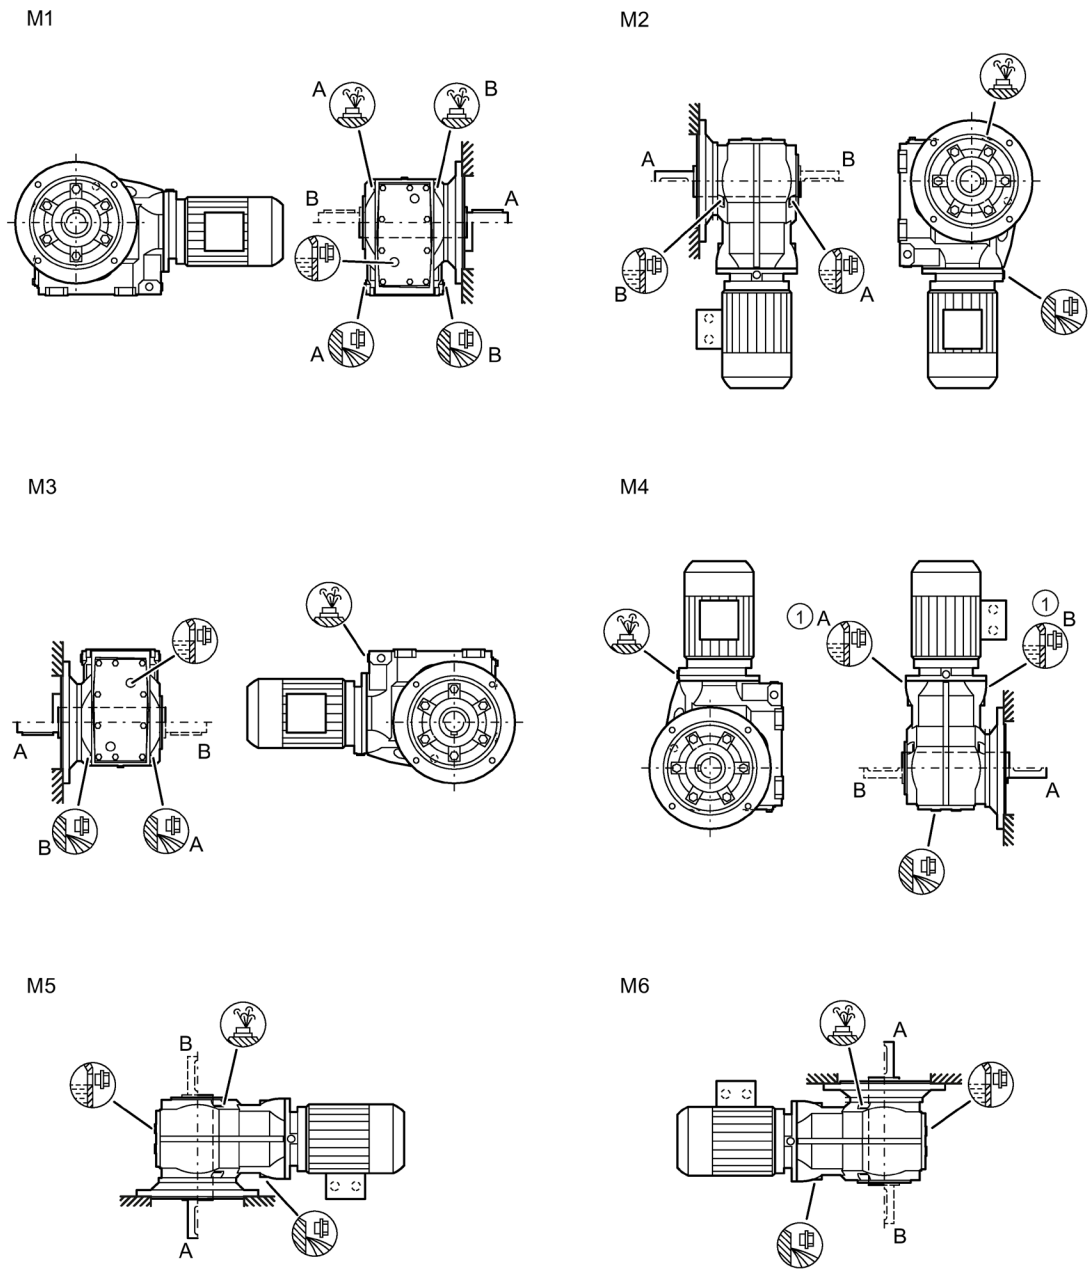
Einbaulagen für Kegelradgetriebe K.F Flanschführung und KAZ mit Gehäuseflansch, Baugrößen 39 - 189
